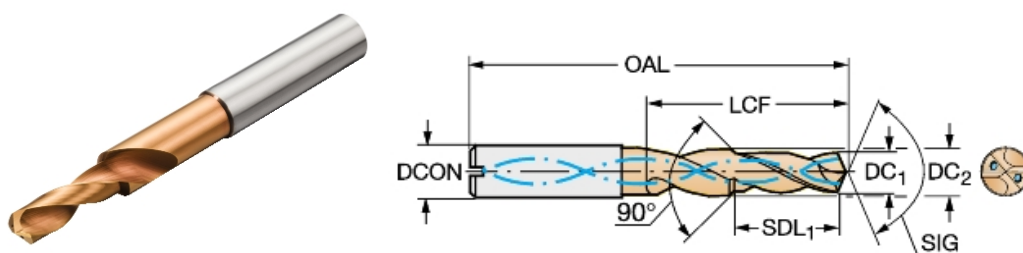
Сверло R841-0555-30-A1A 1220
